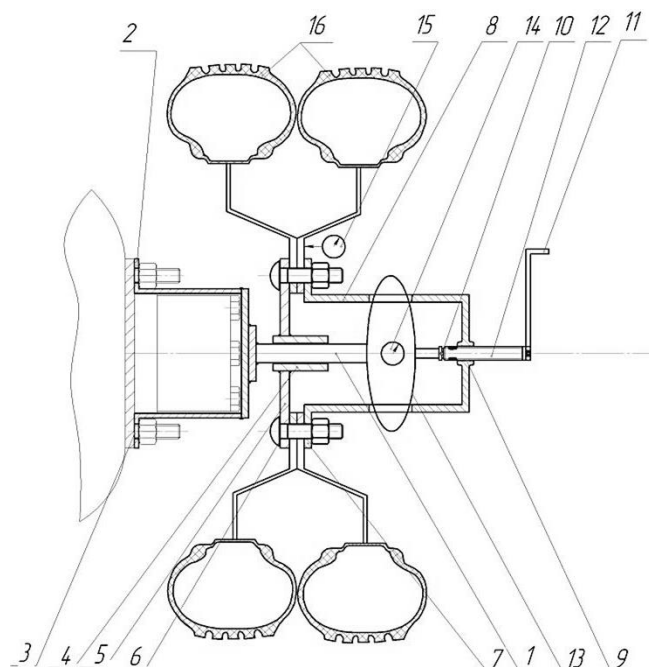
Стенд для определения бокового сцепления и боковой жесткости шин [11]
